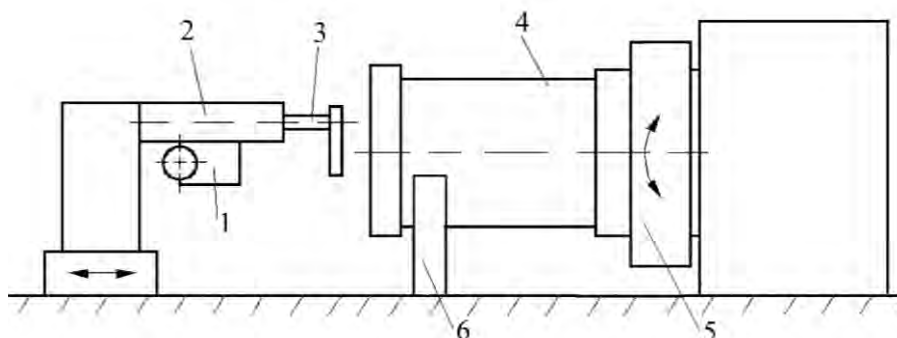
Структура спеціалізованого комплексу для нанесення покриття на внутрішню поверхню циліндричних виробів: 1 – металізатор; 2 – штанга; 3 – маніпулятор; 4 – виріб; 5 – шпindel з патроном; 6 – люнет
